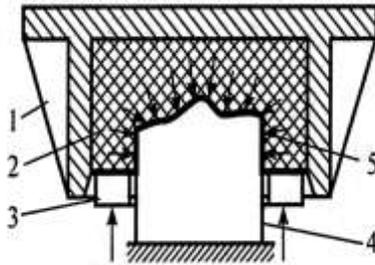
Схема вытяжки эластичной матрицей: 1 – контейнер; 2 – подушка; 3 – прижим; 4 – пуансон; 5 – заготовка
